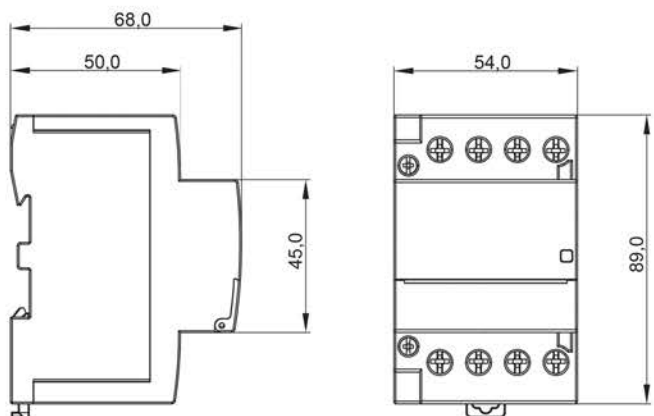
Габаритные размеры контакторов от 40 А до 63 А / Figure 4 – Overall dimensions of contactors from 40 A to 63 A
